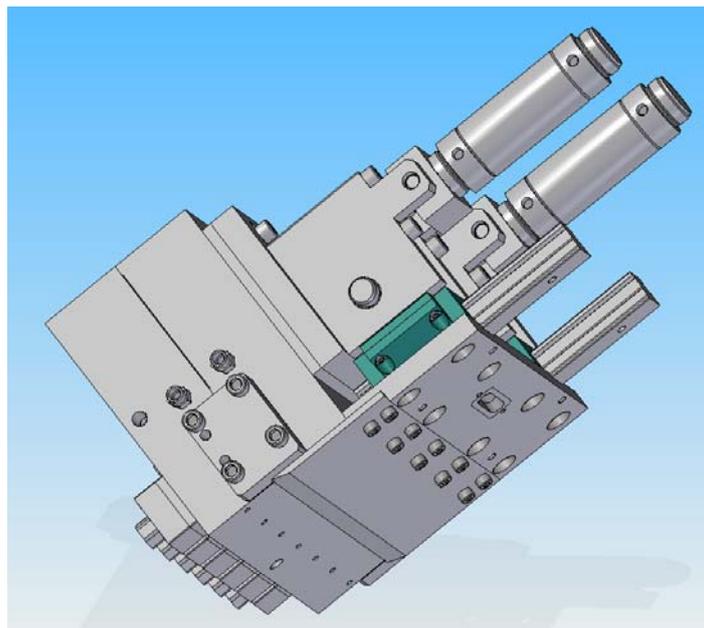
Darstellung der Breitschlitzdüse mit Schaumstrangabschneidevorrichtung
